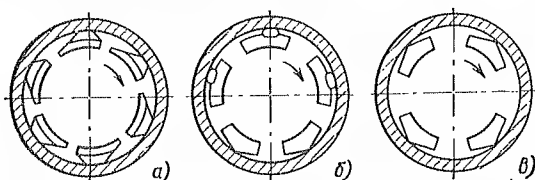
Опорные подшипники с качающимися сегментами:
